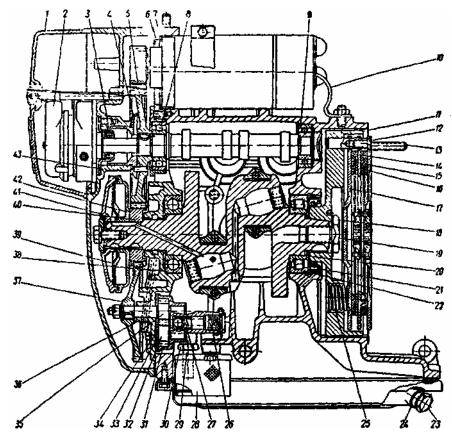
Двигатель МТ801 (продольный разрез): 1 - передняя крышка картера; 2 - прерыватель-распределитель; 3 - сальник распределительного вала; 4 - сапун; 5 - шестерня распределительного вала; 6 - бумажная прокладка; 7 - уплотнительная прокладка генератора; 8 - передний подшипник распределительного вала; 9 - задний подшипник распределительного вала; 10 - упор генератора; 11 - маховик; 12 - винт крепления упорного диска сцепления; 13 - шпилька крепления коробки передач; 14 - ведомый диск сцепления; 15 - промежуточный ведущий диск сцепления; 16 - ведомый диск сцепления; 17 - нажимной ведущий диск сцепления; 18 - болт крепления маховика; 19 - замочная шайба; 20 - маслоотражательная шайба; 21 - сальник коленчатого вала; 22 - задний подшипник коленчатого вала; 23 - сливная пробка; 24 - прокладка; 25 - пружина сцепления; 26 - пружина редукционного клапана; 27 - редукционный клапан; 28 - маслоприемник; 29 - маслозаборная трубка; 30 - гайка крепления трубки; 31 - корпус маслонасоса; 32 - ведомая шестерня маслонасоса; 35 - ведущая шестерня маслонасоса; 36 - корпус переднего подшипника; 37 - шестерня привода маслонасоса; 38 - передний подшипник коленчатого вала; 39 - экран центрифуги; 40 - ведущая шестерня распределения; 41 - крышка центрифуги; 42 - корпус центрифуги; 43 - крышка распределения; 41 - крышка центрифуги; 42 - корпус центрифуги; 43 - крышка распределения; 41 - крышка центрифуги; 42 - корпус центрифуги; 43 - крышка распределения; 41 - крышка центрифуги; 42 - корпус центрифуги; 43 - крышка распределения; 41 - крышка центрифуги; 42 - корпус центрифуги; 43 - крышка распределения; 41 - крышка центрифуги; 42 - корпус центрифуги; 43 - крышка распределения; 41 - крышка центрифуги; 42 - корпус центрифуги; 43 - крышка распределения; 41 - крышка центрифуги; 42 - корпус
